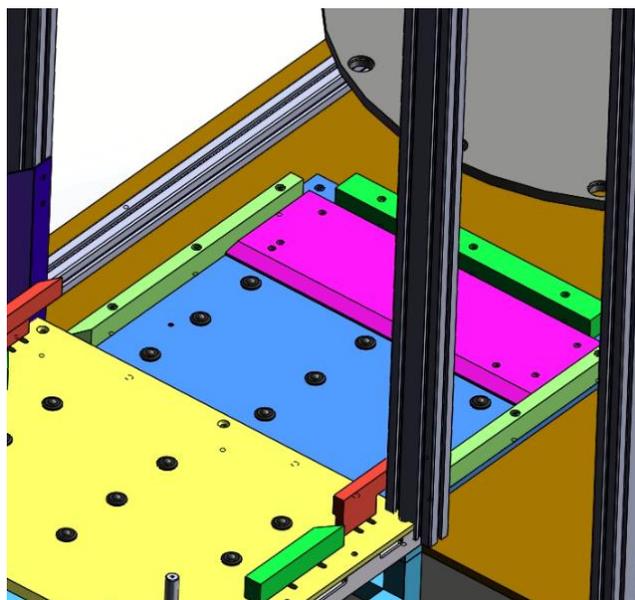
Piecerío sobre la máquina. Fuente:propia
